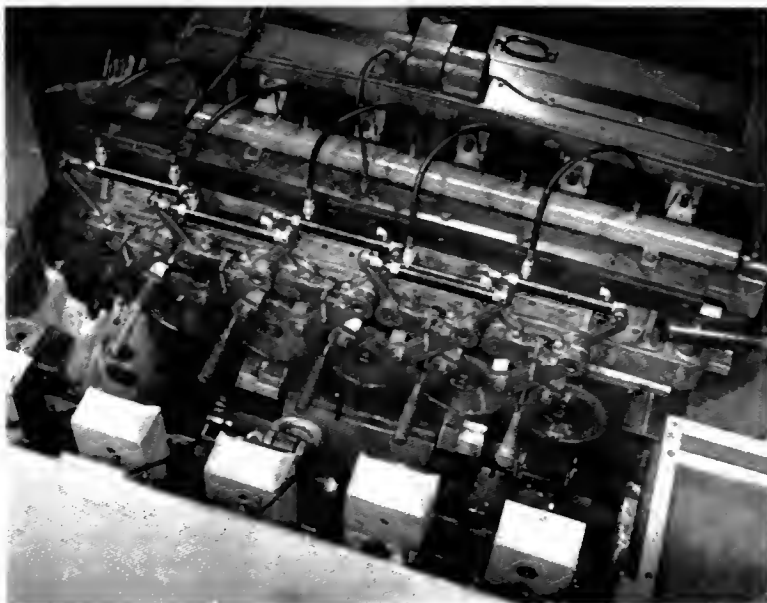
Forgeage de pignons d'attaque à froid (National Machinery Co. — J.G. Kayser)
